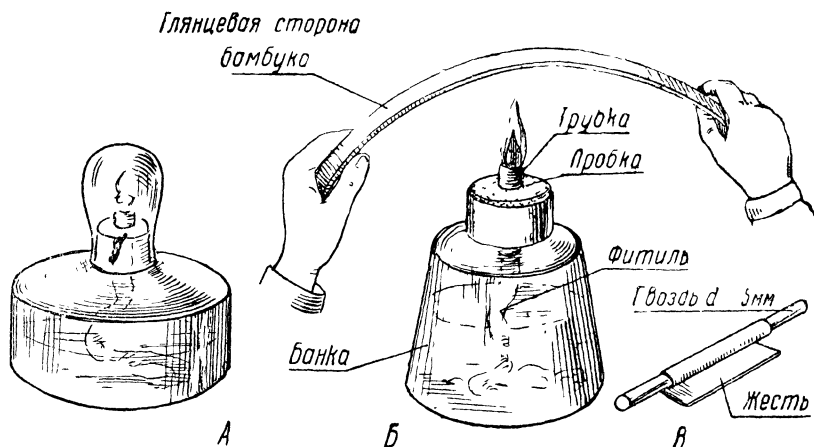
Изгибание бамбука. А — спиртовка, Б — самодельная коптилка, В — изготовление трубочки
